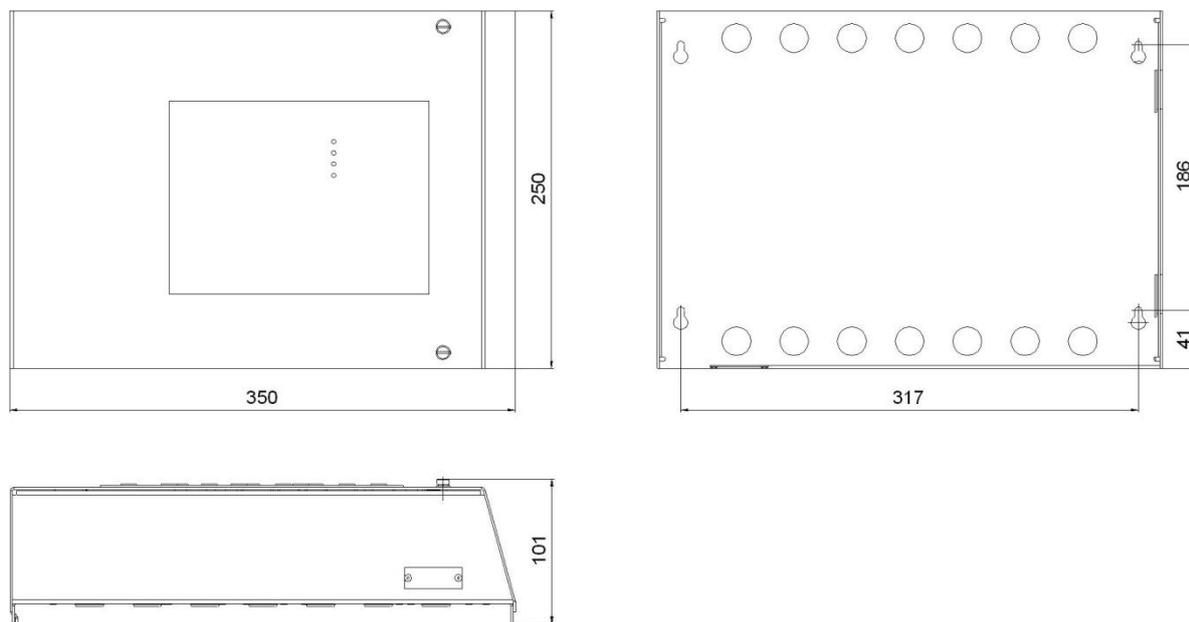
Габаритный чертеж КЛЮ
